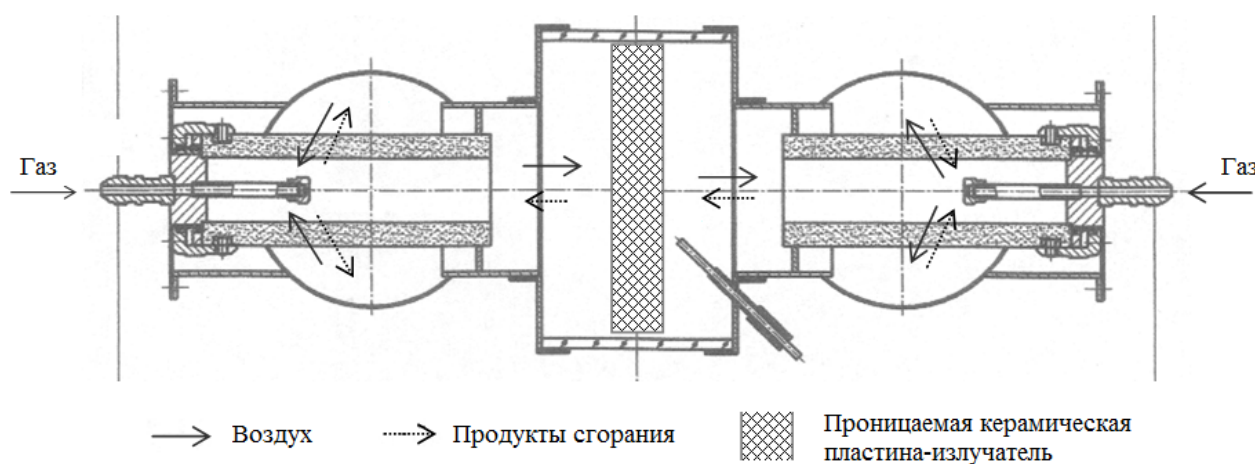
Схема рабочей части камеры сгорания с переменным направлением подачи воздуха
